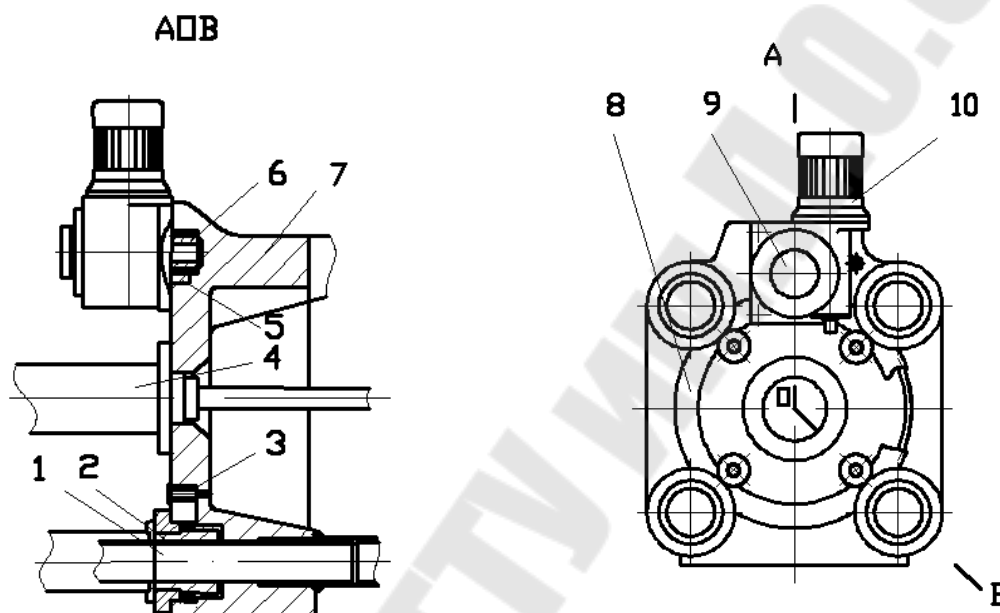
Схема механизма настройки на заданную силу запираения машины ЛПД мод. 71108: 1 - колонна; 2 - гайка; 3 - опорный ролик; 4 - гидроцилиндр; 5 - зубчатое колесо; 6 - приводная шестерня; 7 - задняя плита машины; 8 - кожух шестерни; 9 - редуктор; 10 - электродвигатель
